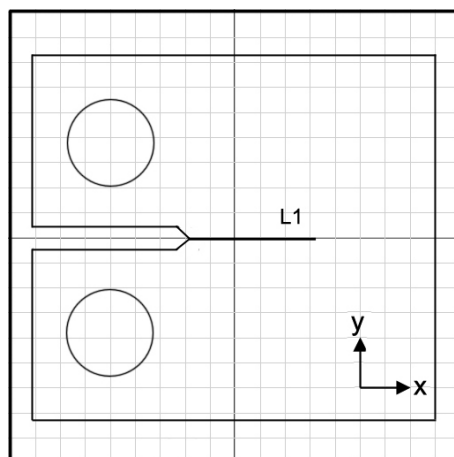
Provete fendado relativo ao ensaio 2, liga Cr-Mn.
